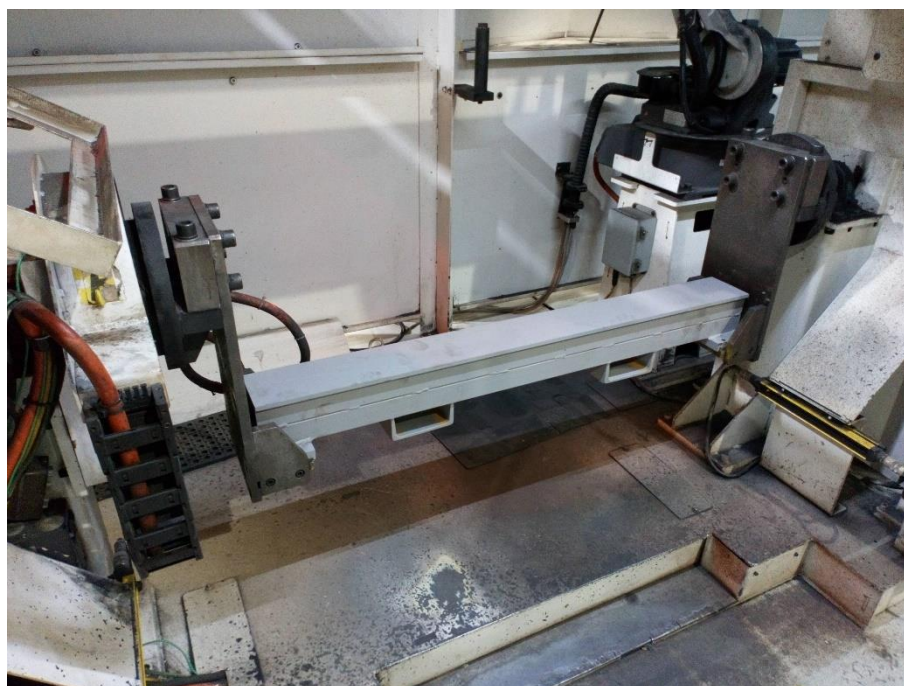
Viga de soldadura con utillajes de sujeción retirados
